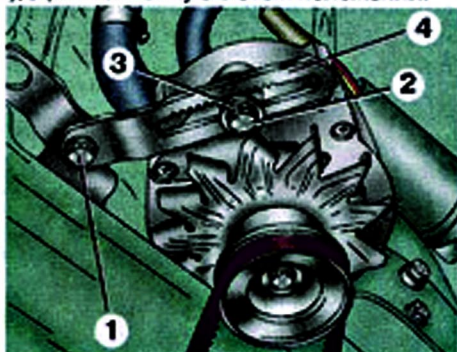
Механизм натяжения ремня привода генератора: 1 – болт крепления кронштейна; 2 – болт механизма натяжения; 3 – гайка регулировочная механизма натяжения; 4 – кронштейн механизма натяжения
